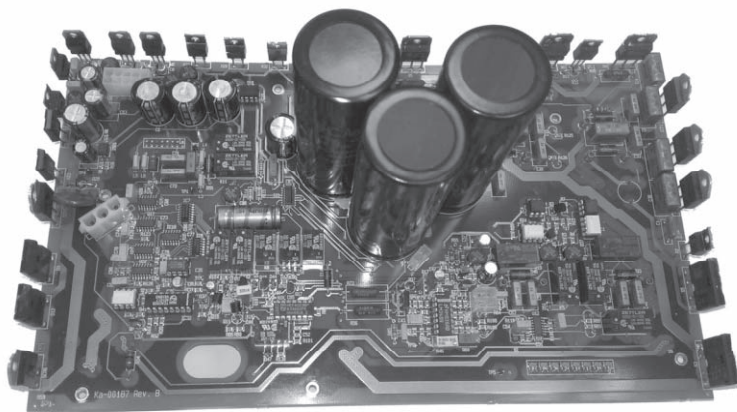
Внешний вид устройства типа V10E для проверки минимального напряжения срабатывания приводов высоковольтных выключателей
